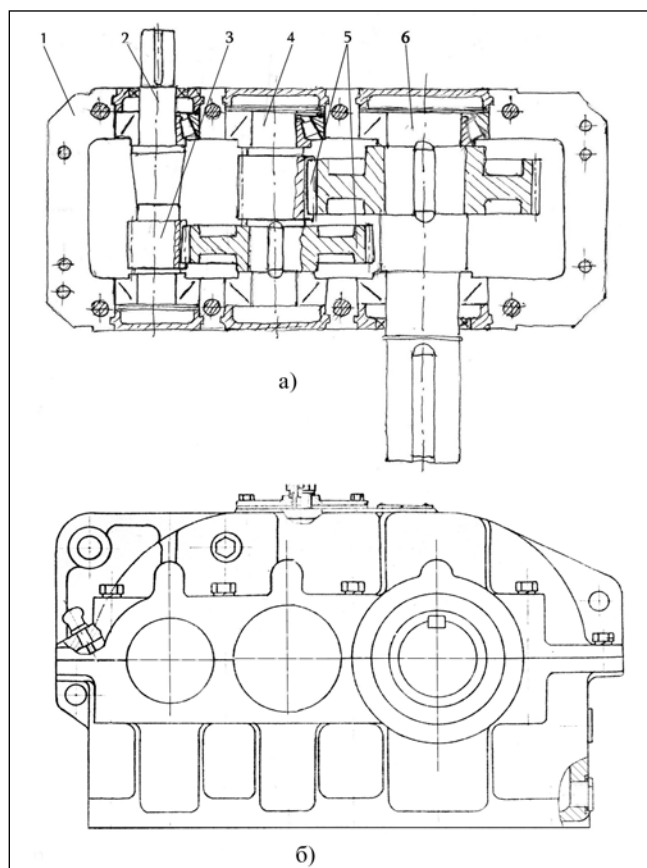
Двухступенчатый редуктор стандартный: а) продольный разрез, б) общий вид
